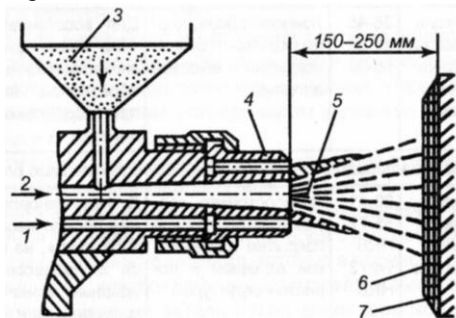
Схема газопламенного напыления порошкового материала:
